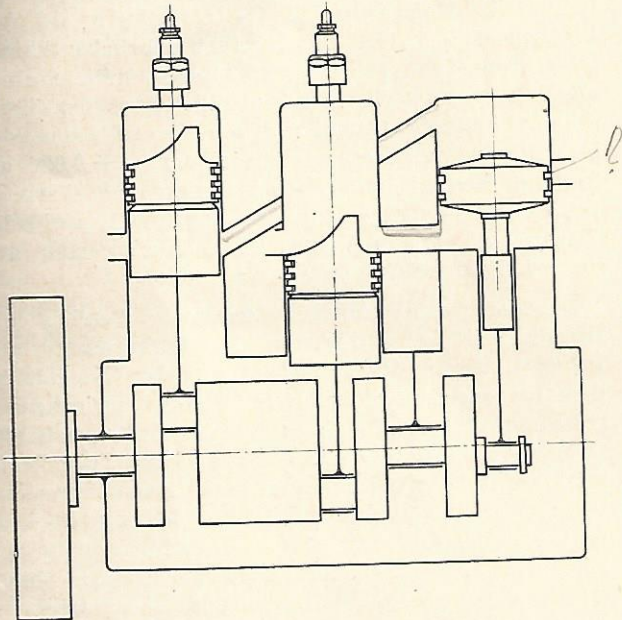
Schema einer Zylindergruppe des DKW-Motors, Type KB 1000
